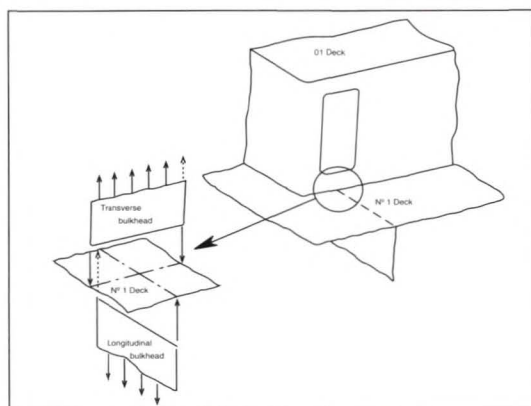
Agrietamiento unión superestructura destructor tipo 81.
